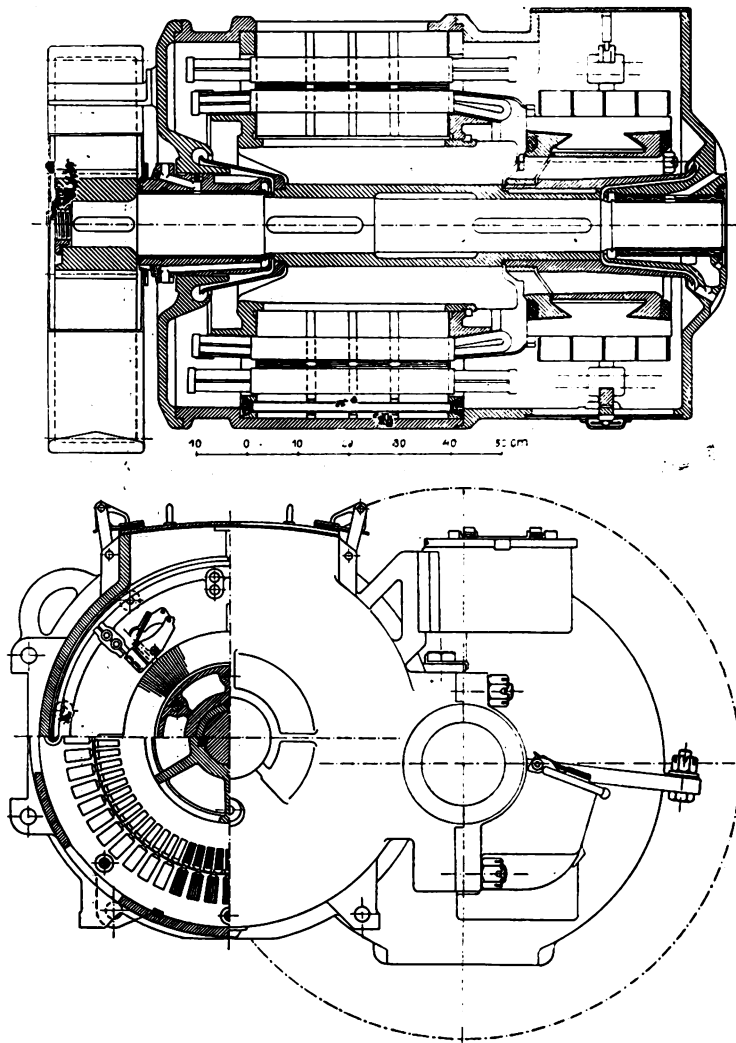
et 16. — Coupe et vue de côté d'un moteur de 225 chevaux de la locomotive n° 2.
